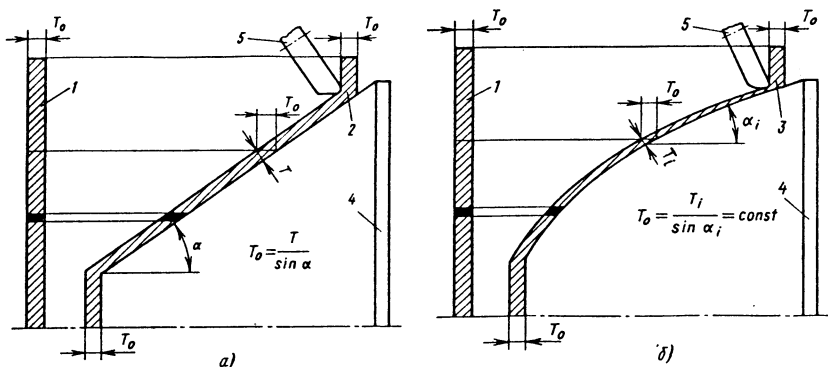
Схема ротационной вытяжки из плоской заготовки конической (а) и оживальной (б) формы:
